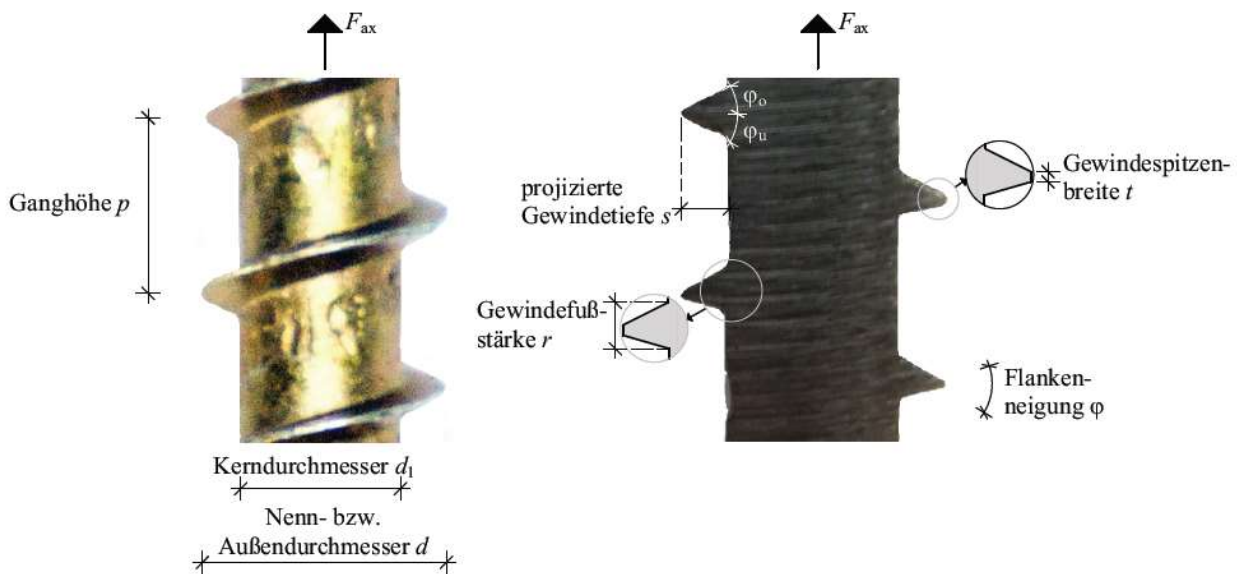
Geometrieparameter des Gewindes, am Beispiel einer typischen selbstbohrenden Holzschraube
